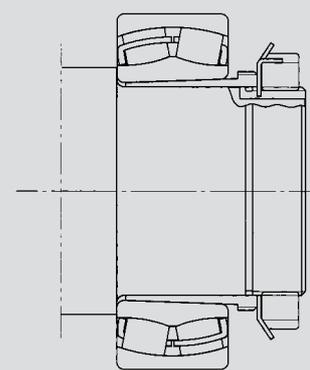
Цилиндрический вал, стопорная шайба (стяжная втулка)
